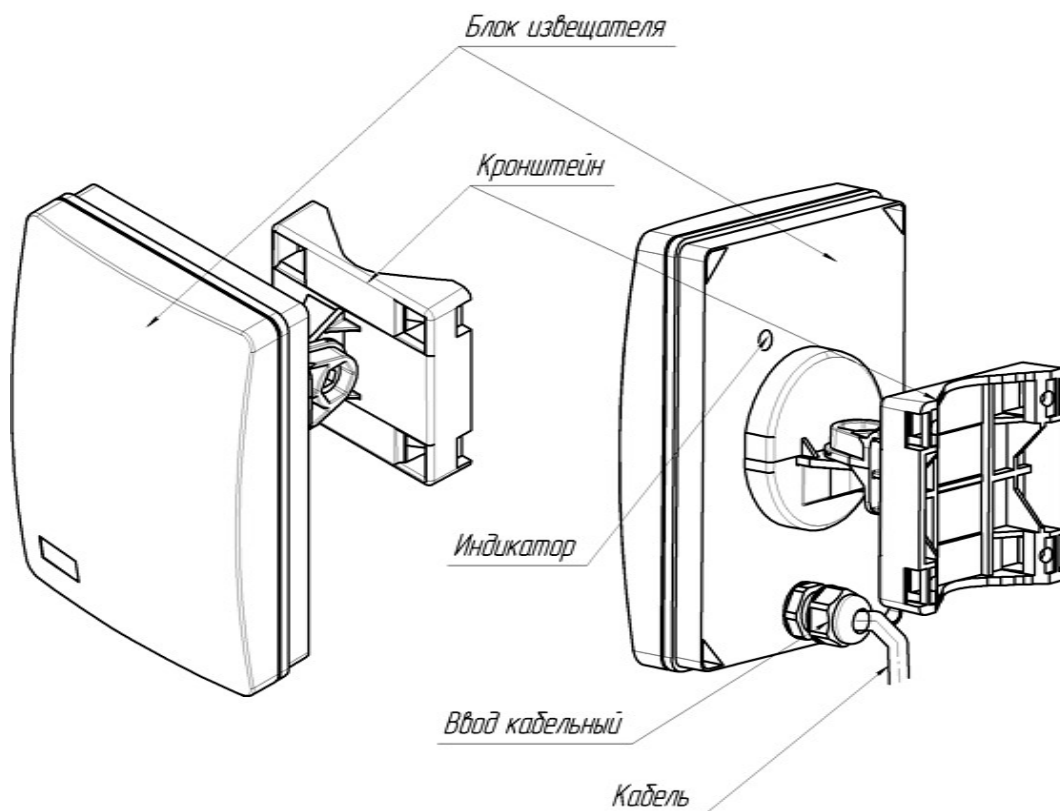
Внешний вид блока (ПРМ, ПРД) извещателя
